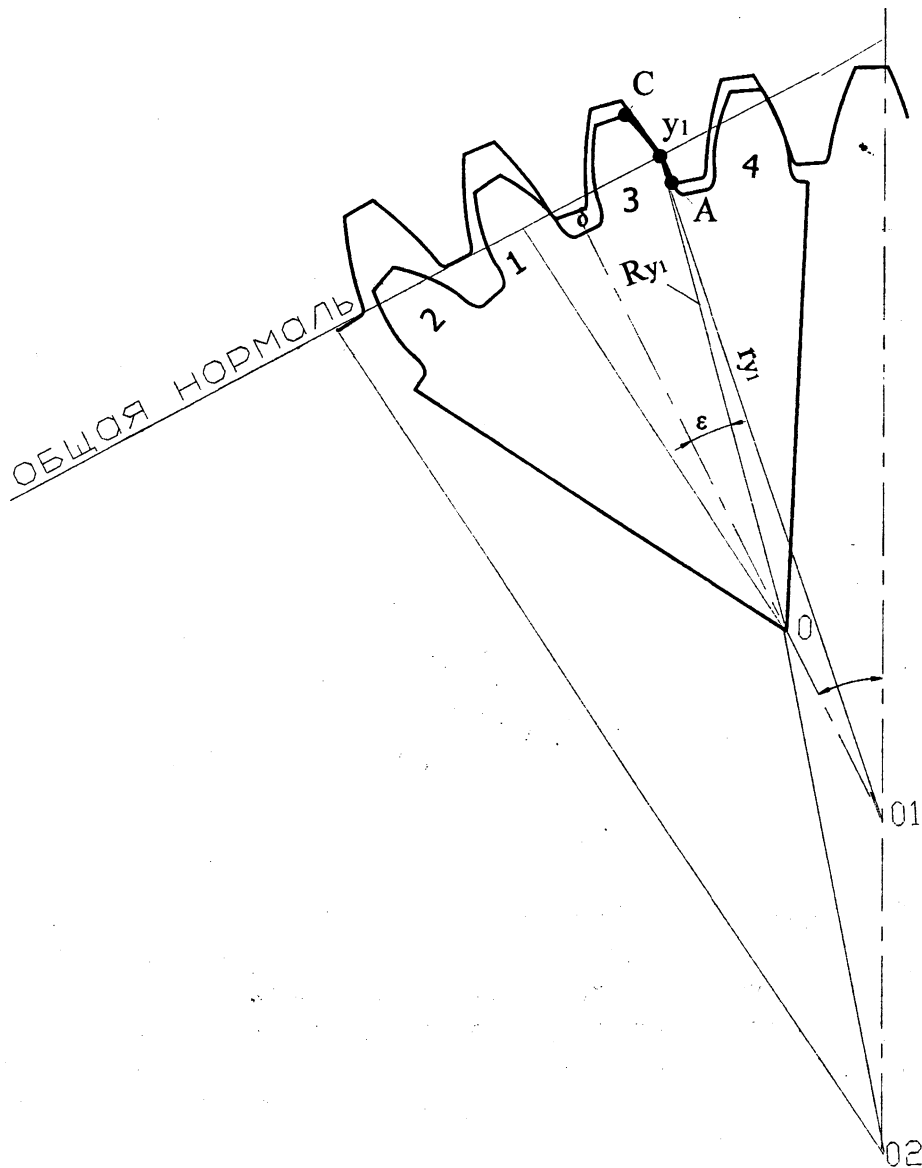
Зацепление зубьев зубчатого сектора и цельного зубчатого колеса внутреннего зацепления
